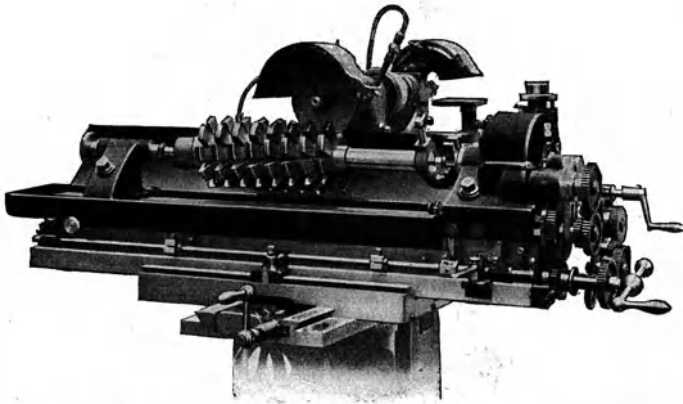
Die Reineckerschärfmaschine mit selbsttätigem Teilapparat.
